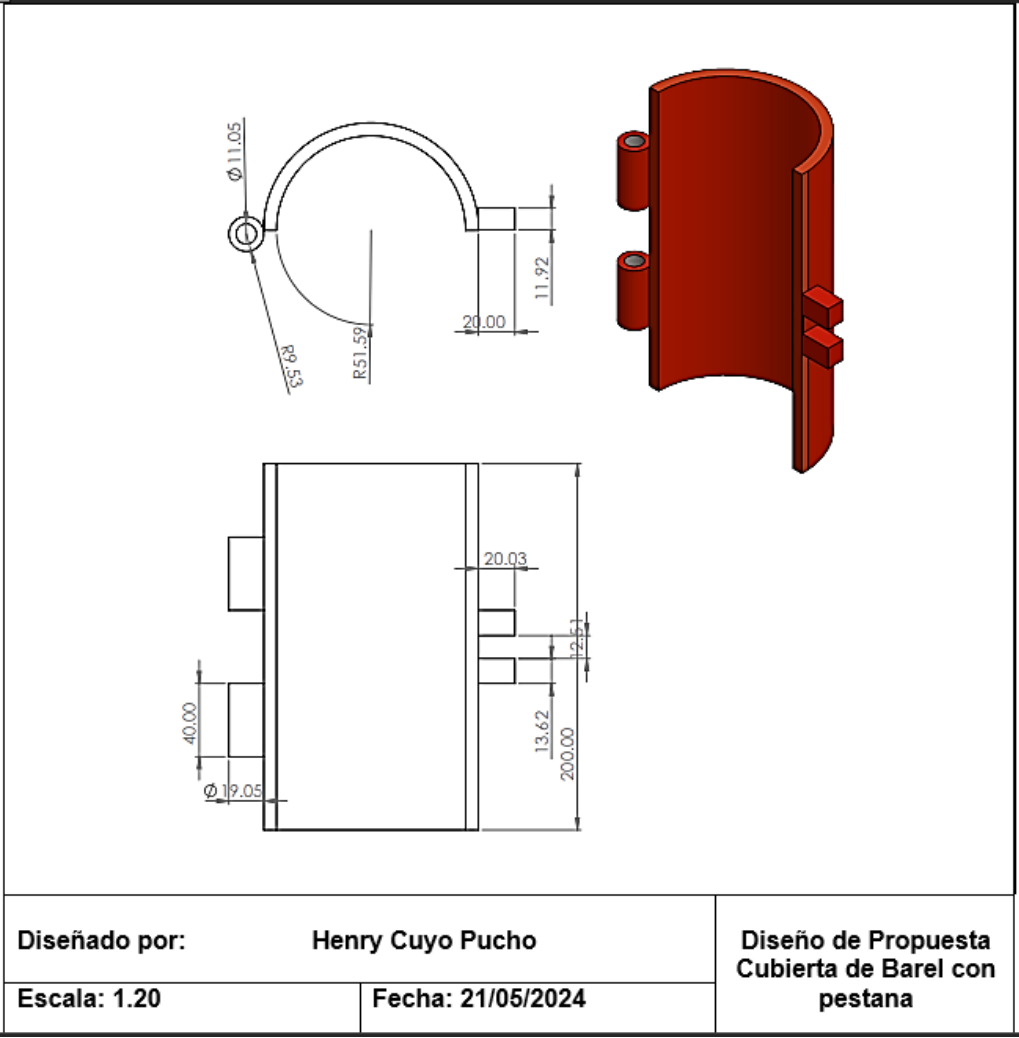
Plano de cubierta de Barel para armado de Covered Base for Barel – CBB.
